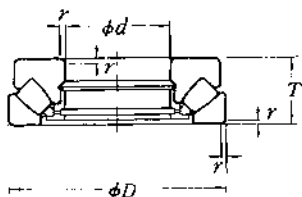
Сферические упорные подшипники с бочкообразными роликами
